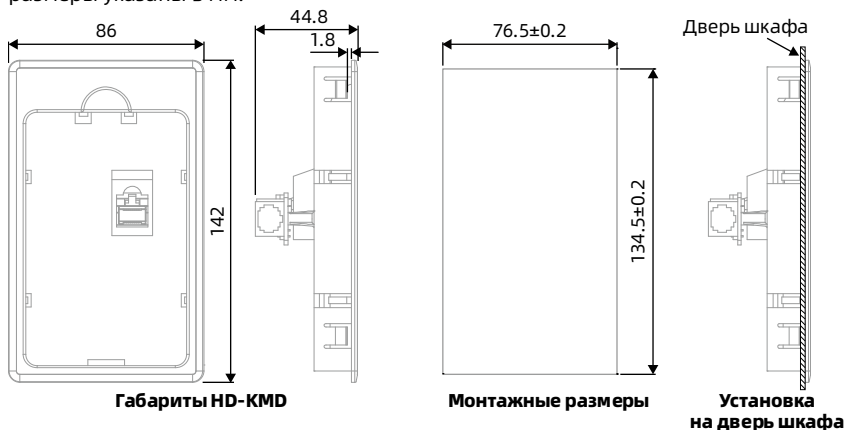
Габаритные и монтажные размеры HD-KMB
